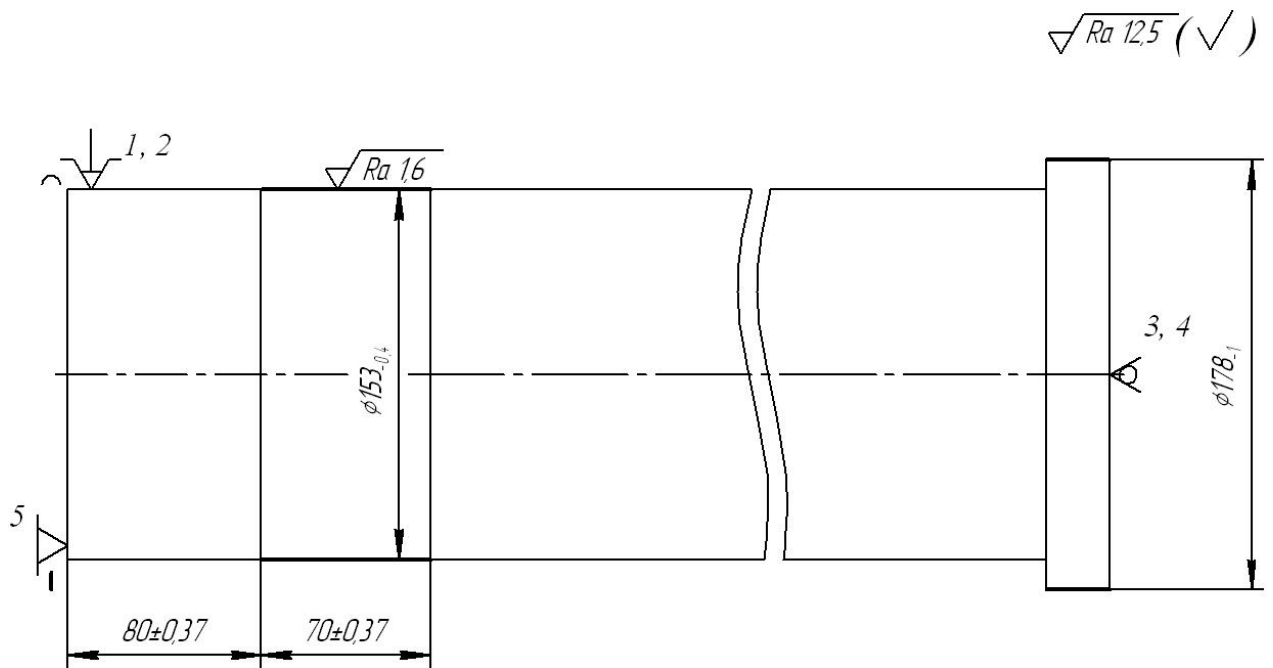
Альтернативна схема базування заготовки на операції токарно-гвинторізній 020, установ Б
